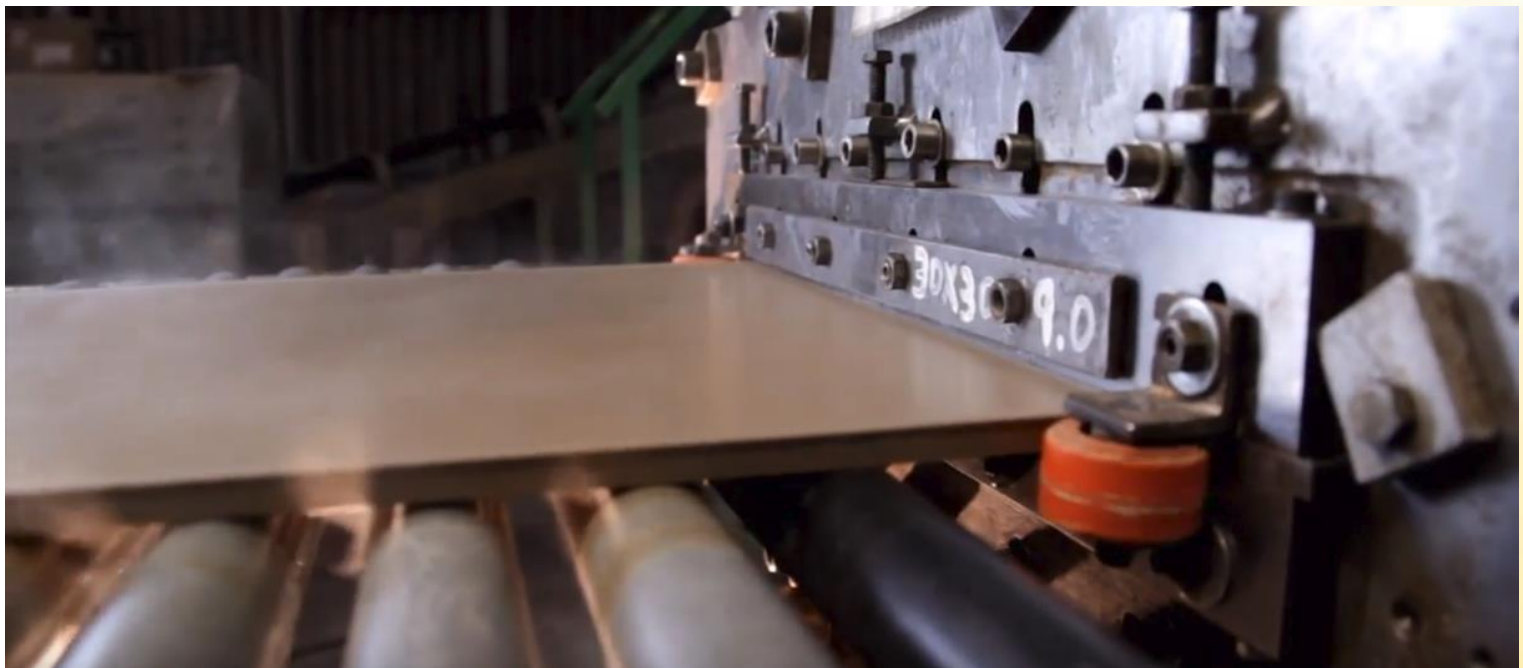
Калибрующее устройство, с сечением для базовой плитки
